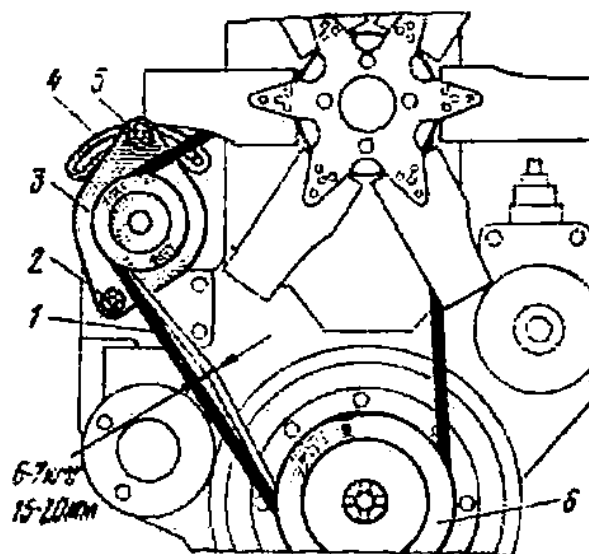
Устройство для натяжения ремня привода вентилятора и генератора двигателя СМД-14
